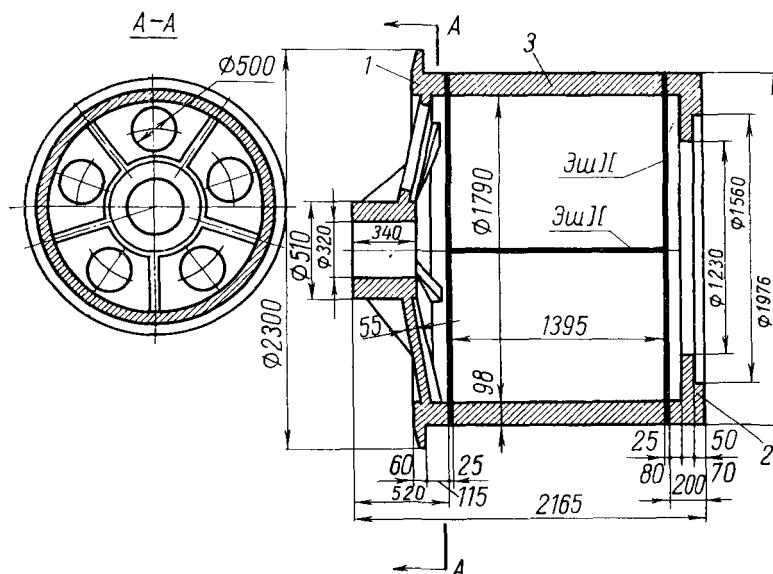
Сварной барабан лебедки шагающего экскаватора ЭШ-25-100
